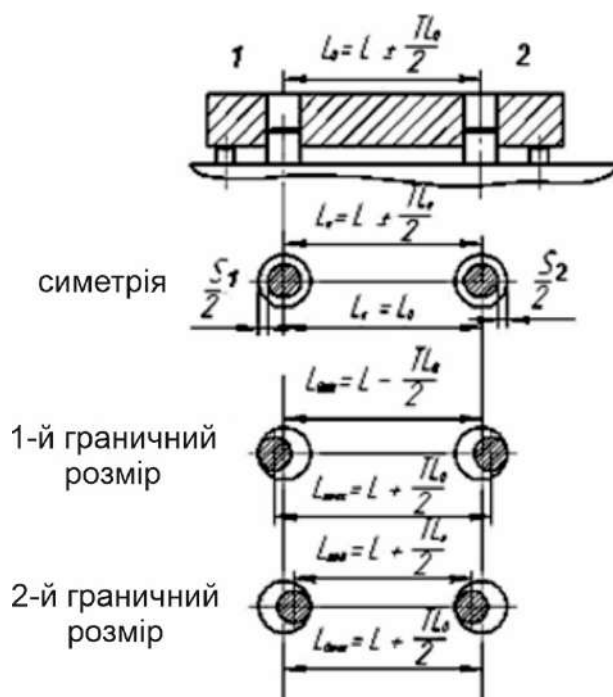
Розрахункова схема установки на два циліндричні пальці
